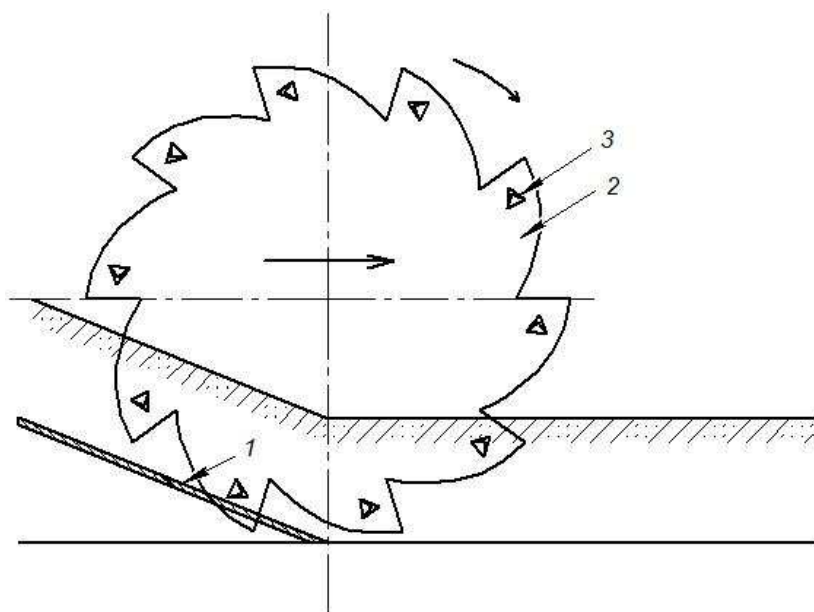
Зубчатый диск с почвозацепами (1 – лемех; 2 – зубчатый диск; 3 – почвозацеп) (патент на пол. мод. № 134735) [8]
